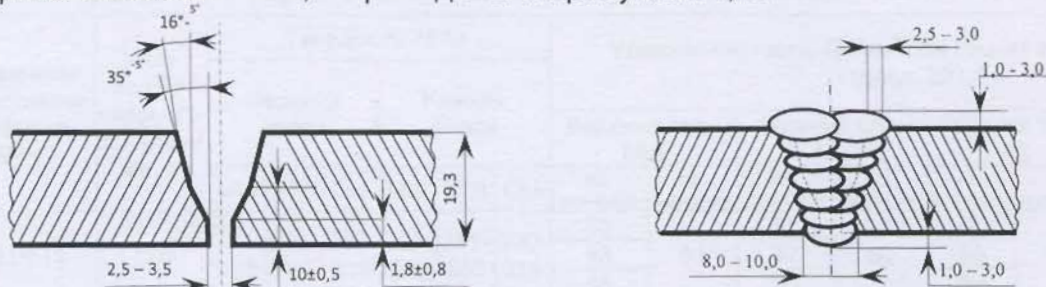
Геометрические параметры сборки контрольного сварного соединения и эскиз сварного шва КСС № 1
